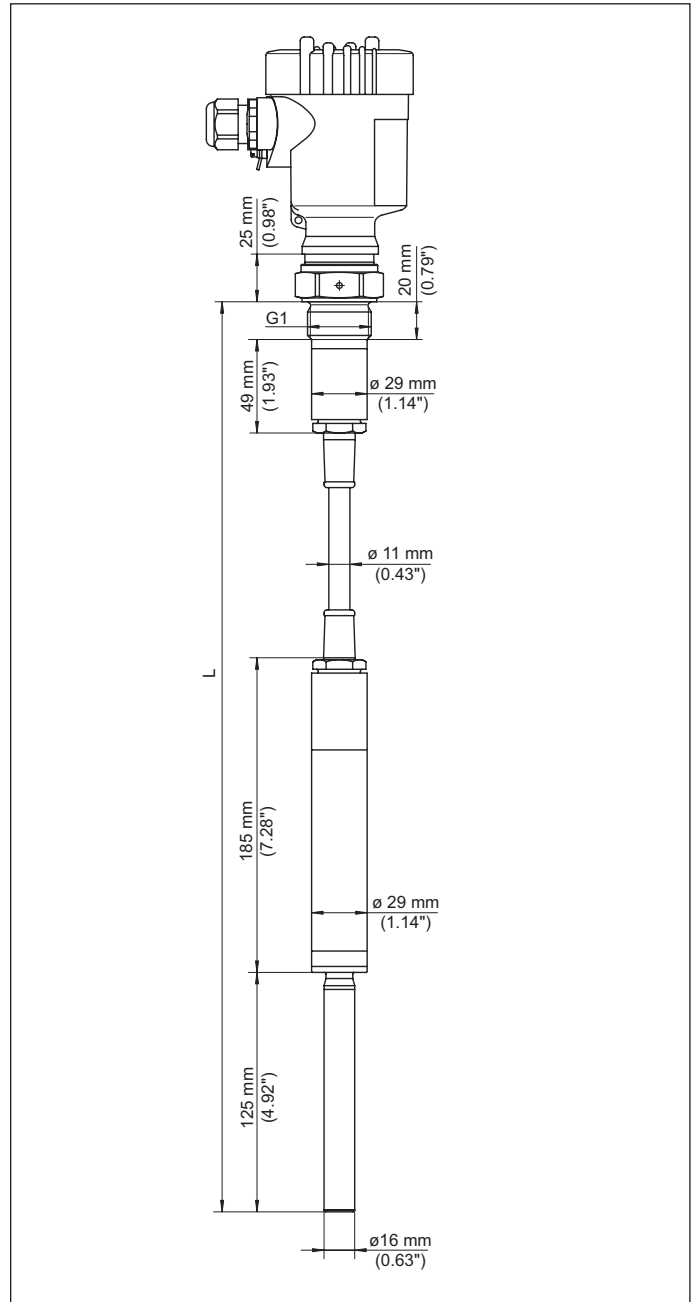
VEGAVIB 62 - Gewindeausführung G1
